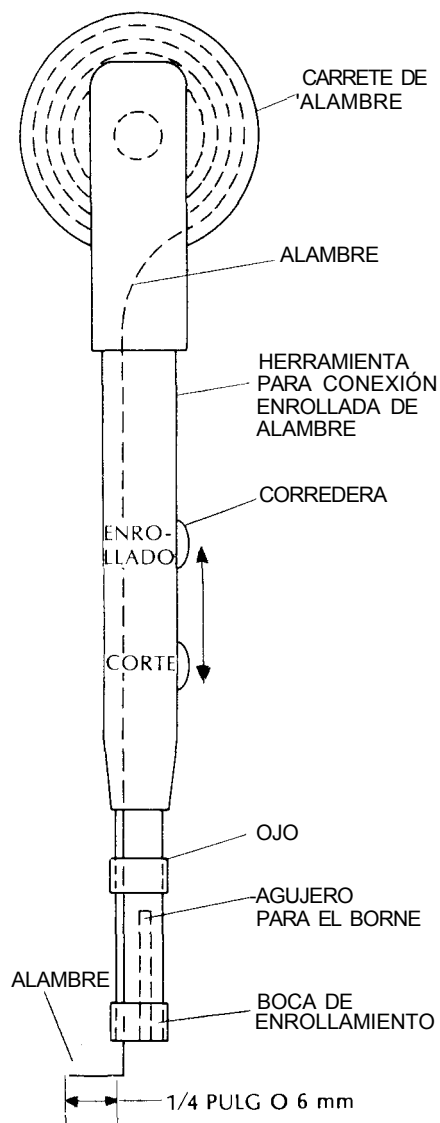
Alambre insertado en la herramienta para conexión enrollada.
